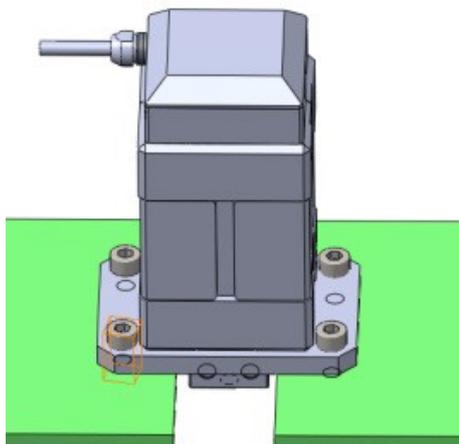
Beispiel für Montage mittels Montageflansch B (räumliche Ansicht)
